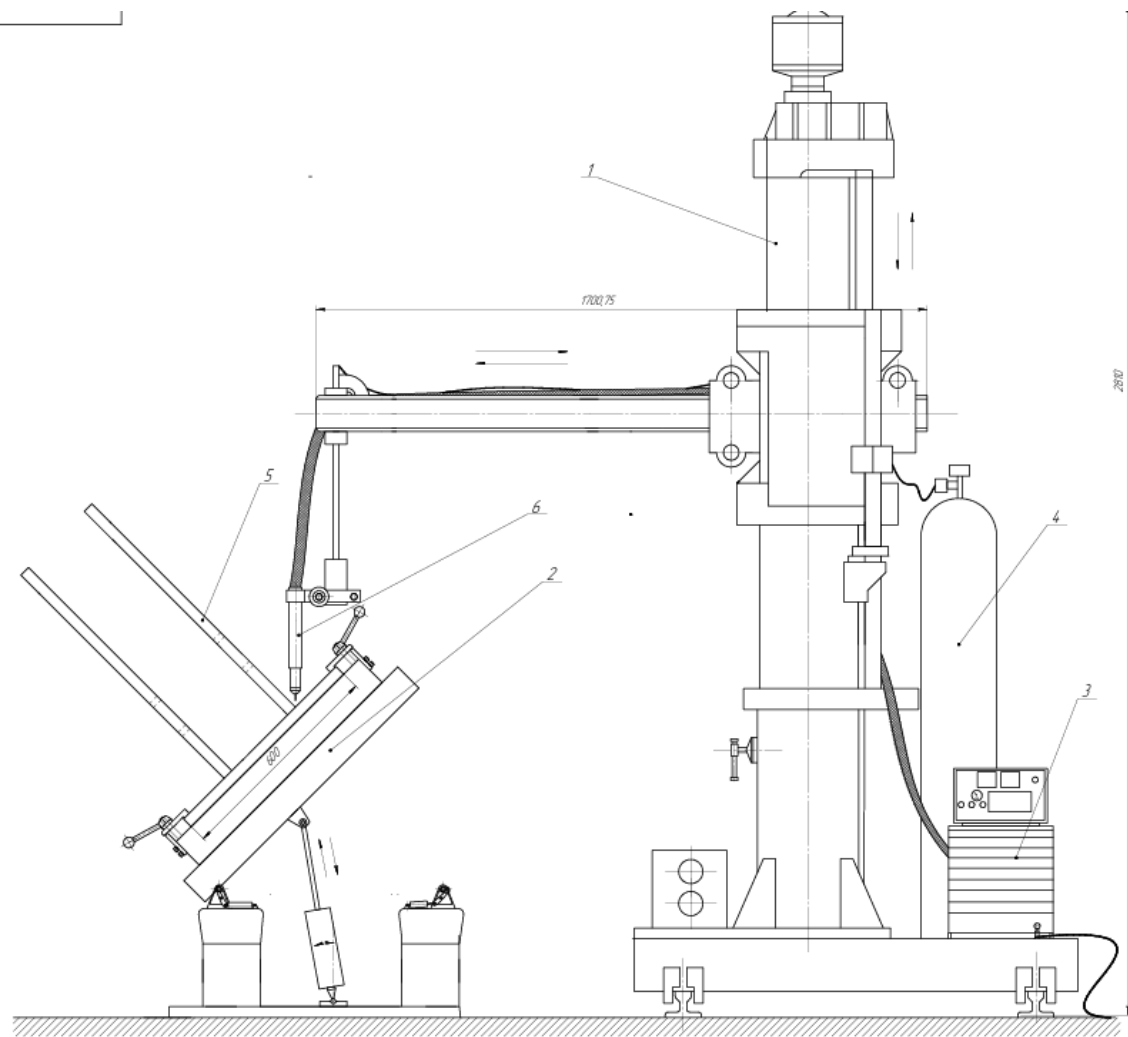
Схема установки для зварювання елемента рамної конструкції
